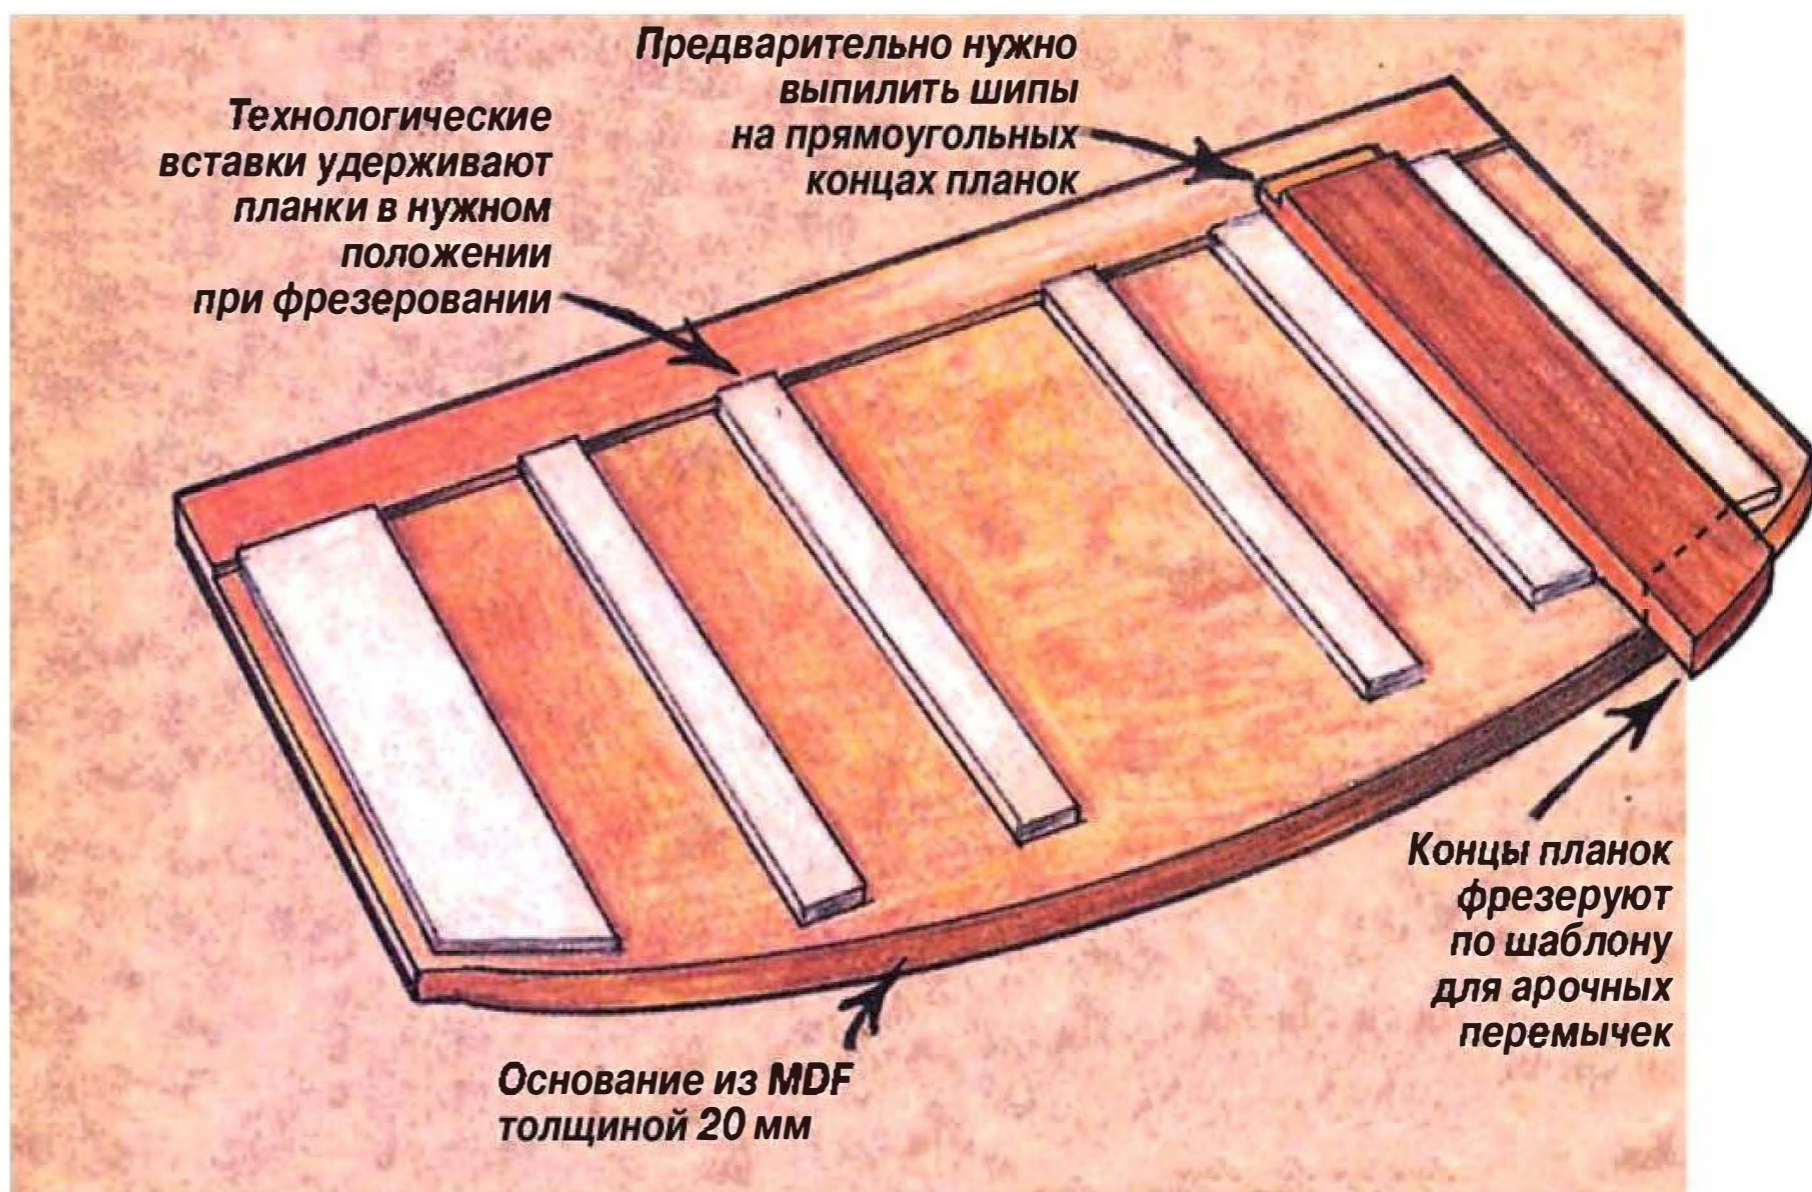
Приспособление для фрезерования торцов боковых планок.
